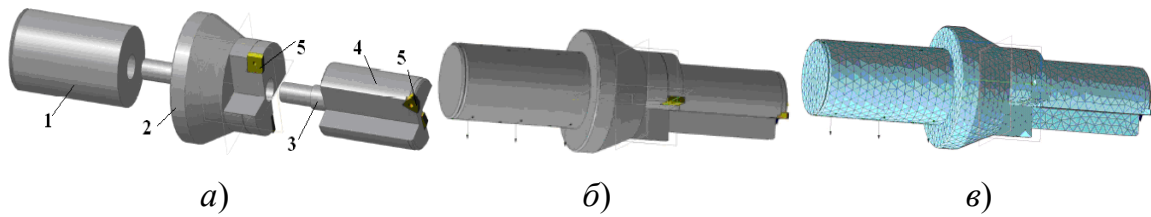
Схемы для расчета НДС комбинированного инструмента с конической соединительной и цилиндрической центрирующей частями:
